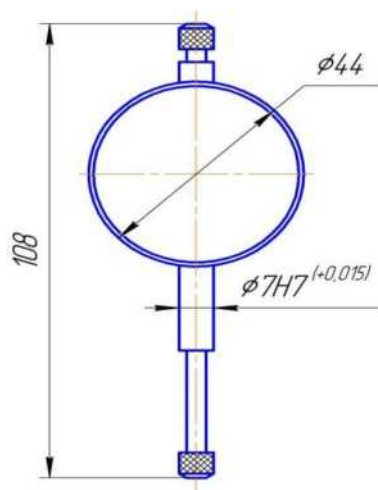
Габаритні розміри індикатора багатообертового моделі 2МИГ-1
